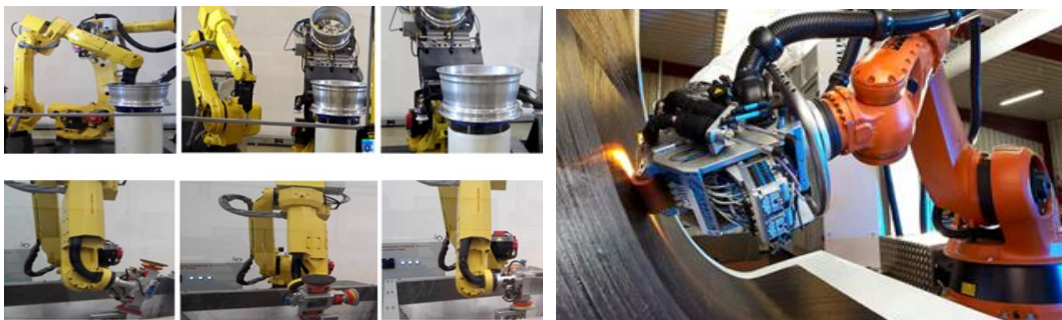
Fig. Izda.: Estación de desbarbado; Dcha.: Robot de pulido. Fabricante SINOVO
